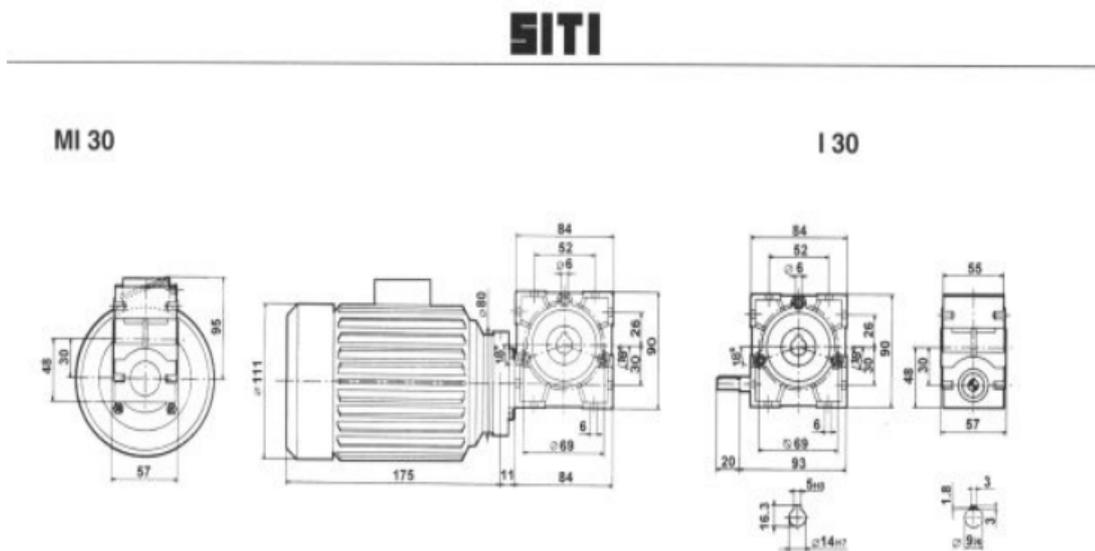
Dimensiones del reductor que origina vaivén en el conjunto cuchilla de producto.
